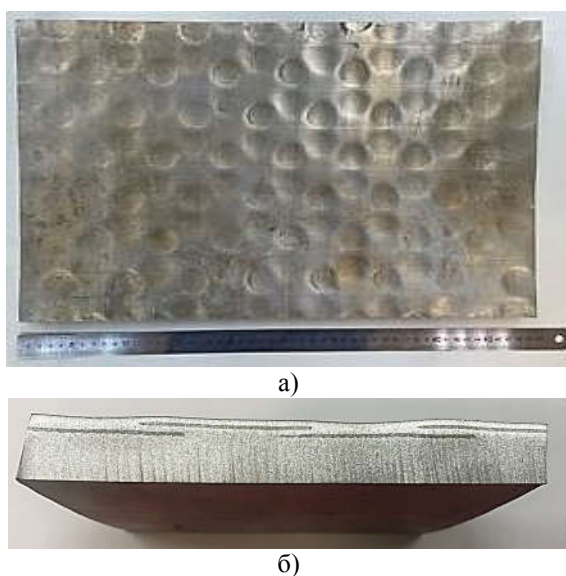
Фотографии экспериментального образца композиционного металлического материала после сварки взрывом и гидроабразивной резки: а – внешний вид композита; б – поперечный срез композита в плоскости перфораций в армирующих слоях
